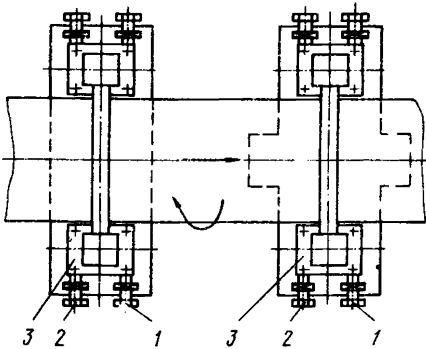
Схема регулировки положения корпуса барабанной сушилки
